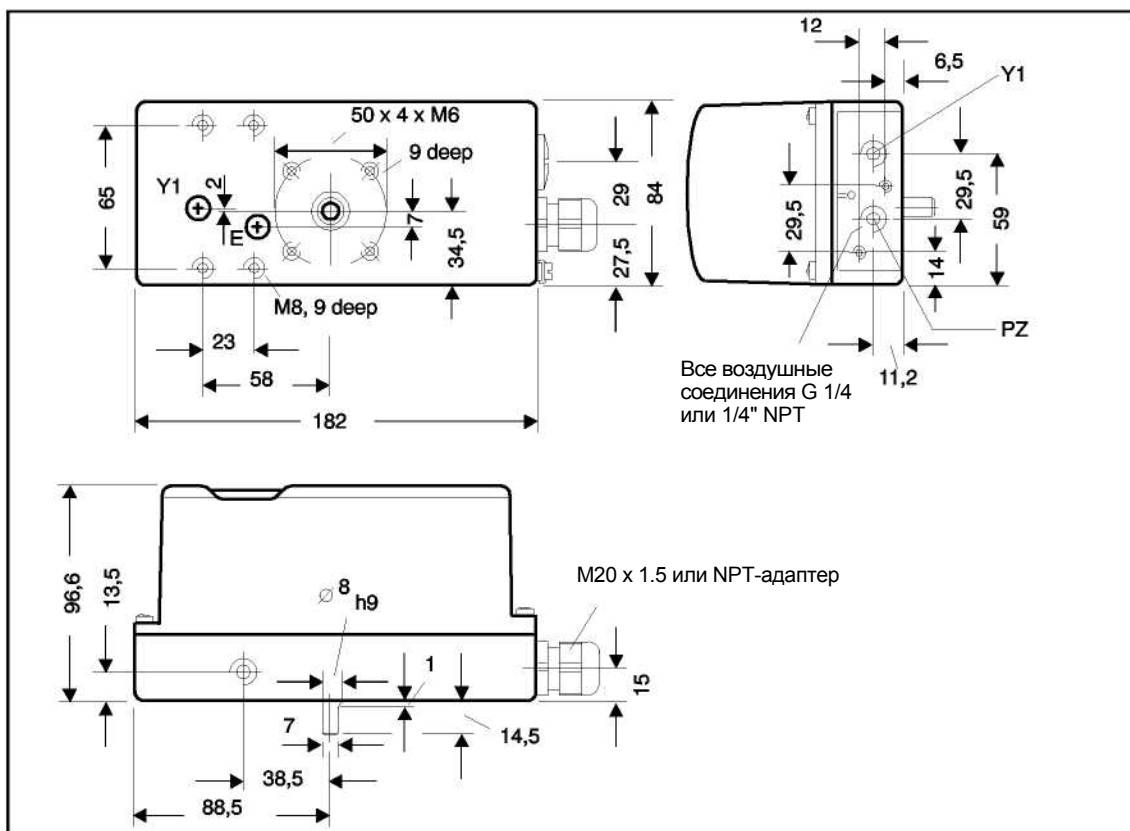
Размерный чертёж версии с металлическим корпусом 6DR5xx1
